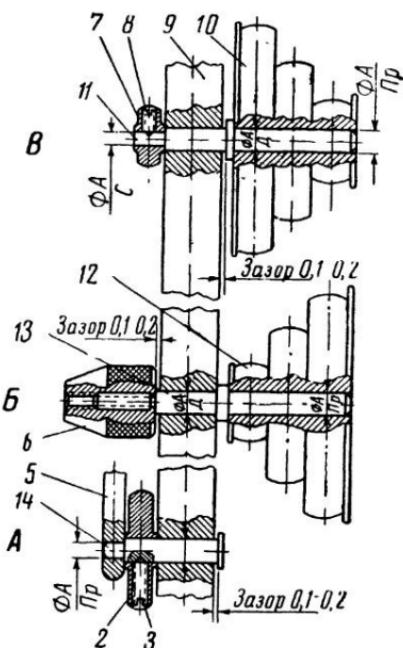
Модель плоскоременной передачи со шкивами (схема соединения деталей): А — узел привода (2 — ведущий шкив привода, 3 — стопорный винт, 5 — рычаг привода, 14 — ведущий вал); Б — узел рабочего вала (6 — гайка, 12 — ведущий шкив рабочего вала, 13 — рабочий вал); В — узел ведущего вала (7 — ведомый шкив привода, 8 — стопорный винт, 9 — стойка, 10 — ведущий шкив рабочего вала, 11 — ведущий вал передачи).
